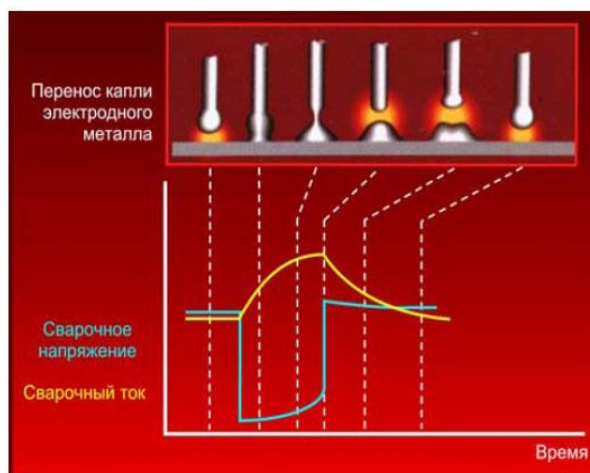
Типичные формы кривых сварочного тока и напряжения при традиционном способе полуавтоматической сварки [10]
